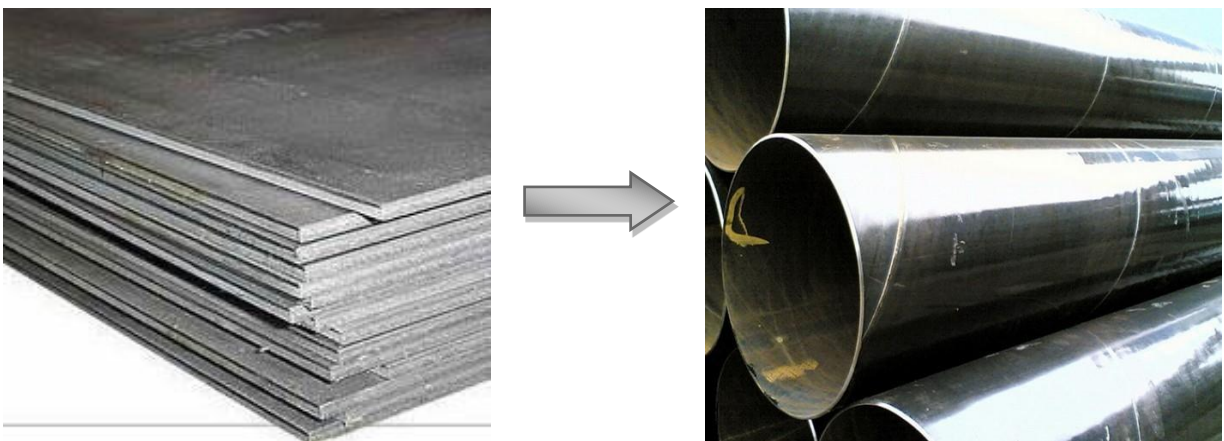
De la plaque au tube en acier [BEL 12]
